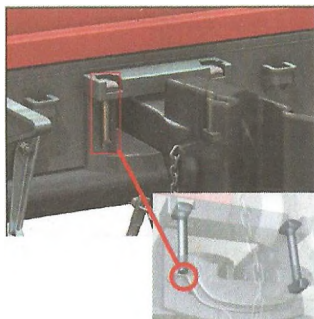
Излом или трещина центрирующей балочки, маятниковой подвески (или направляющей рейки центрирующего прибора безмаятникового типа), неправильно поставленные маятниковые подвески (широкими головками вниз)
